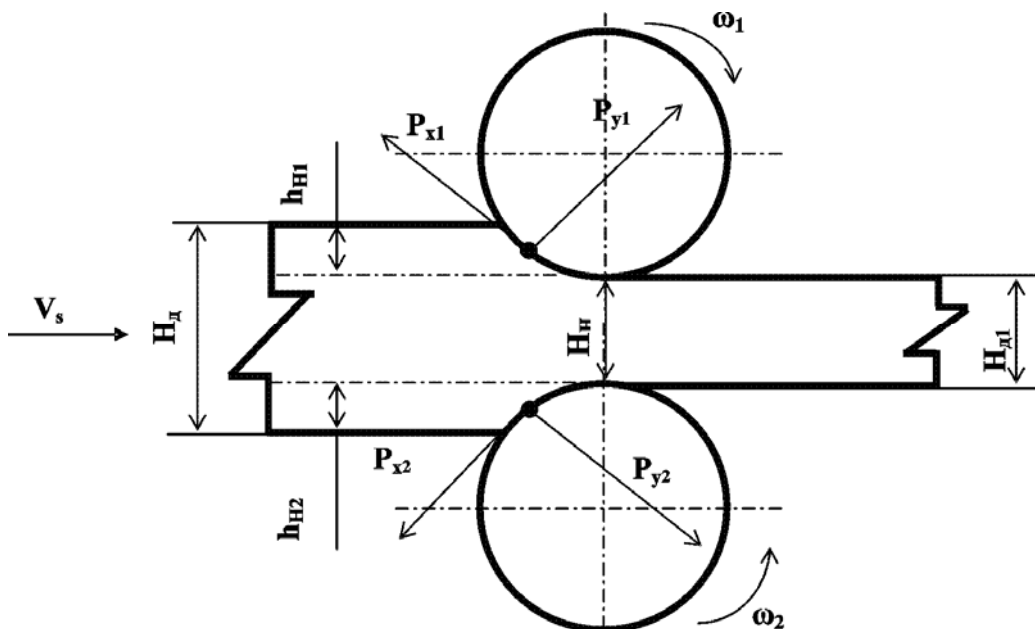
Технологічна схема оброблення двома шліфувальними інструментами:
